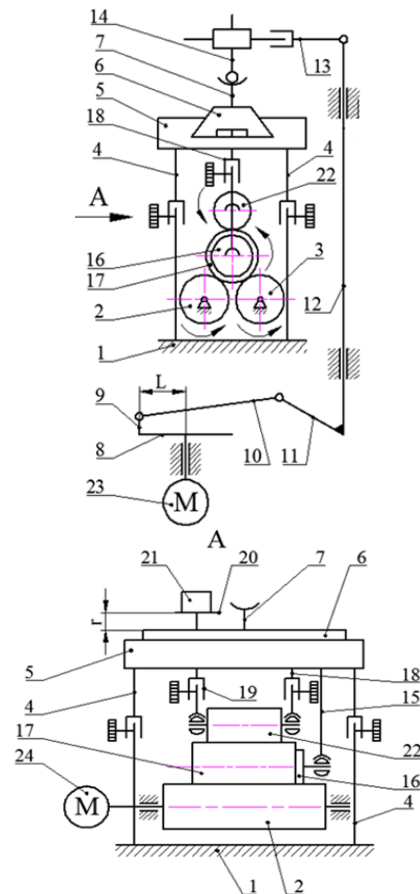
Станок для изготовления деталей из заготовок цилиндрической формы:
